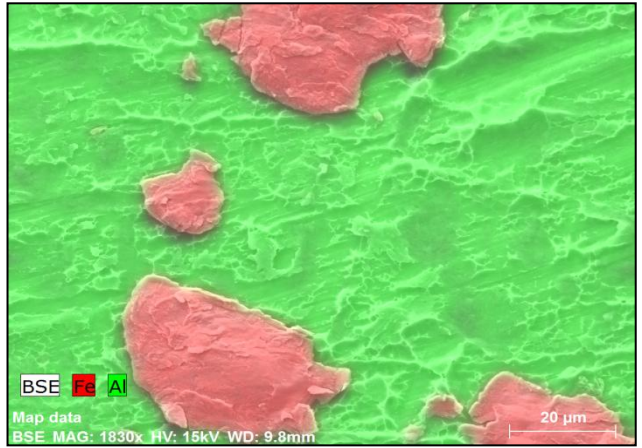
Superfície de fratura do alumínio. Soldas sem preaquecimento.
